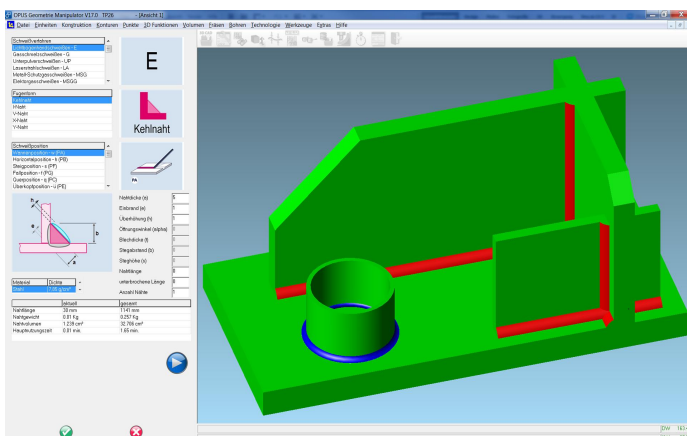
Auslegung der Kehlschweißnähte im Falle des Lichtbogenhandschweißens (Quelle: R+B GmbH, Dernbach)
